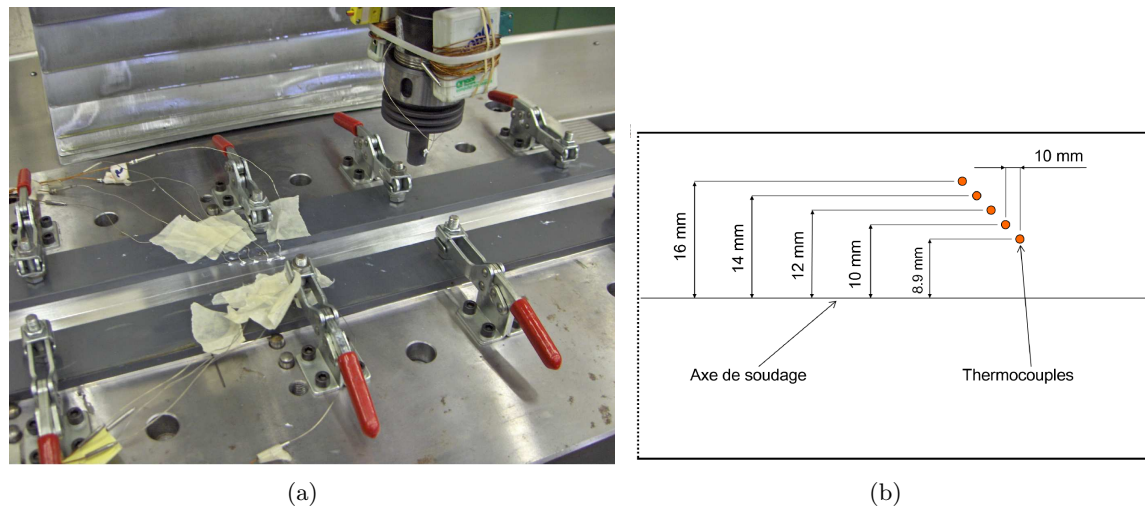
(a) Photographie de la machine de soudage et de l'appareillage de mesure.
